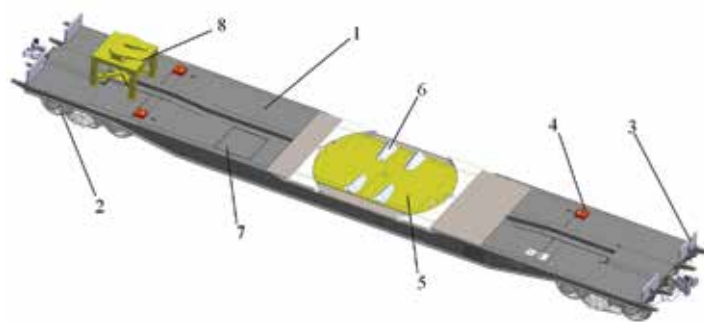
Платформа модели 13-9938: 1 – рама; 2 – тележка; 3 – откидной торцевой борт; 4 – фитинговый упор; 5 – поворотная погрузочная площадка; 6 – упор колесный; 7 – ящик для упоров; 8 – тумба с седельным устройством
